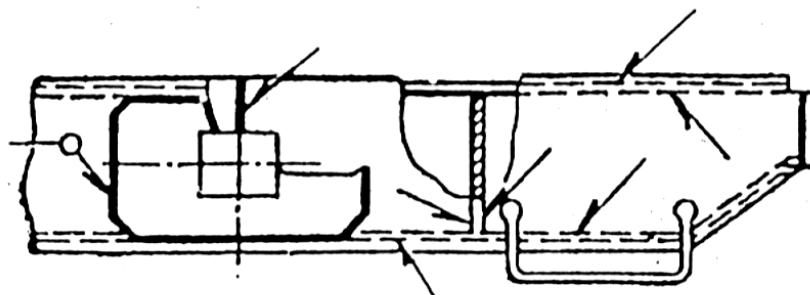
Вертикальный лист балки сварной конструкции, отремонтированный путем замены половины листа и усиленный накладкой
